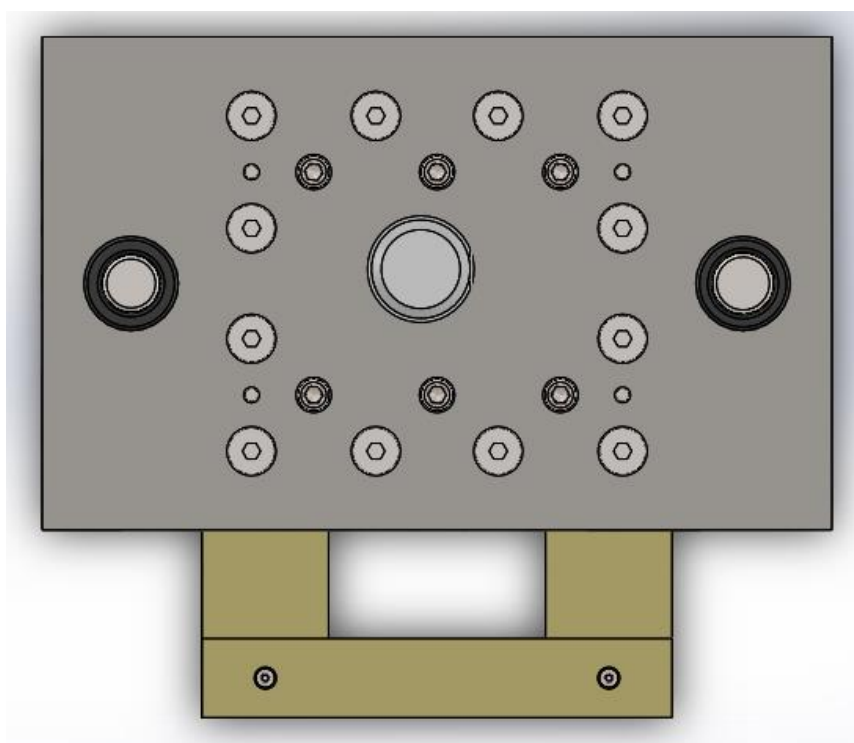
Vista en planta del troquel. Fuente: Elaboración propia
